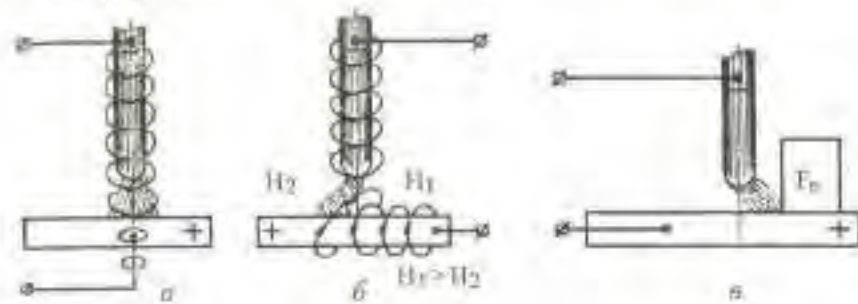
Вплив магнітного поля на зварювальну дугу.
